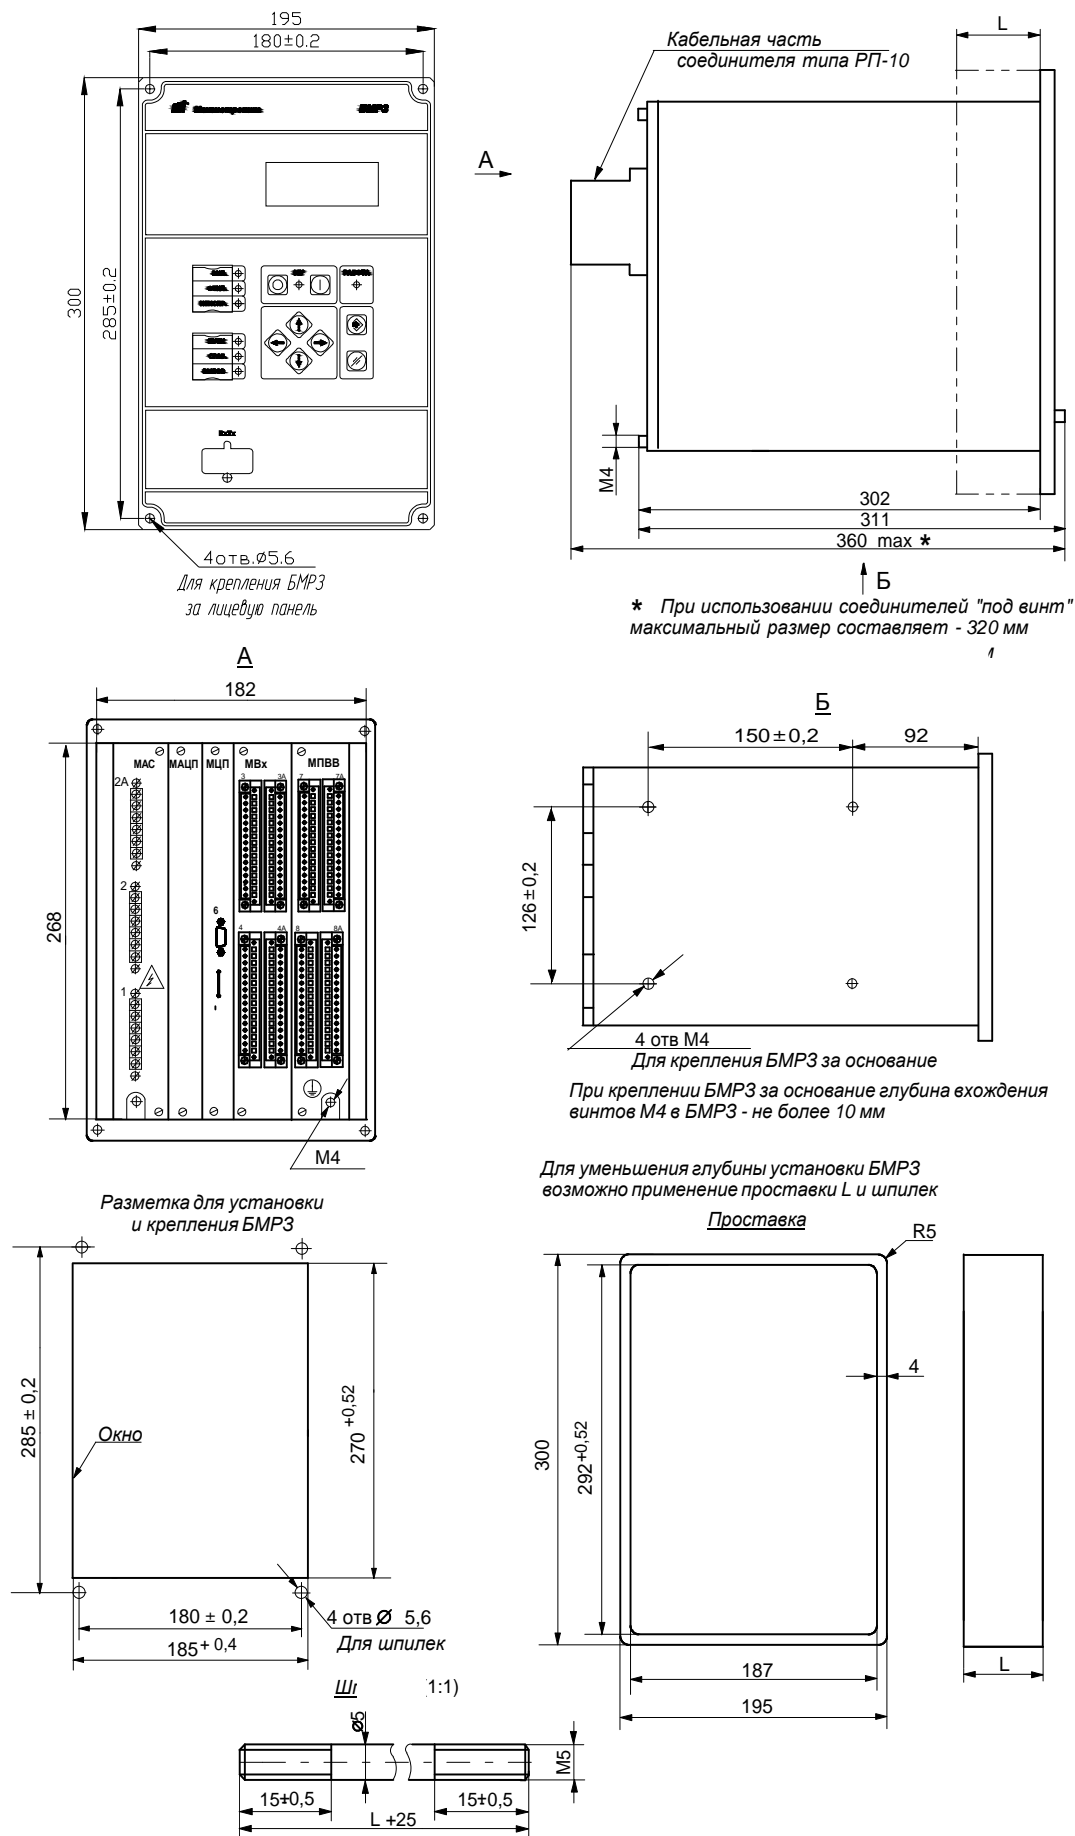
(лист 1 из 3) а – Габаритные, присоединительные и установочные размеры БМР3
